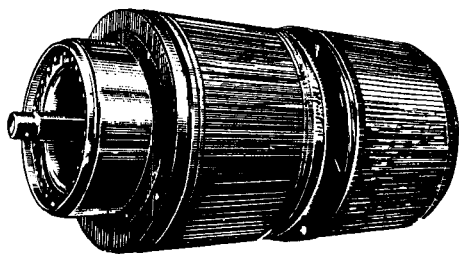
Соединительные сопротивления, смонтированные на втулке якоря: 1—сопротивление; 2—втулка; 3—отверстие для пропуска потока воздуха
